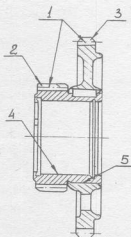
Шестерня ведущая привода распределительного вала в сборе с промежуточной
